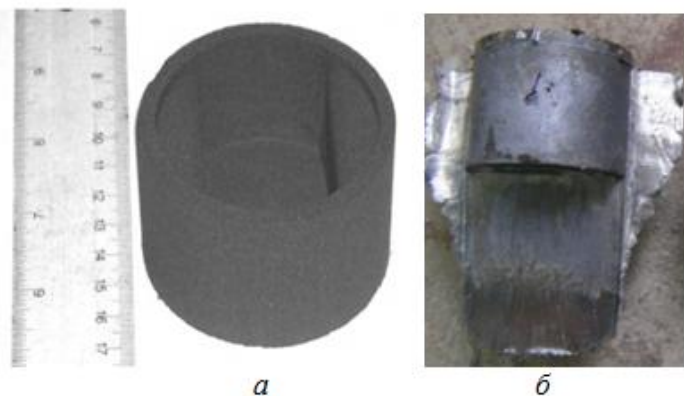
Зовнішній вигляд поковок поршня компресора (а) та пера лопатки (б), отриманих гарячим штампуванням спечених заготовок
